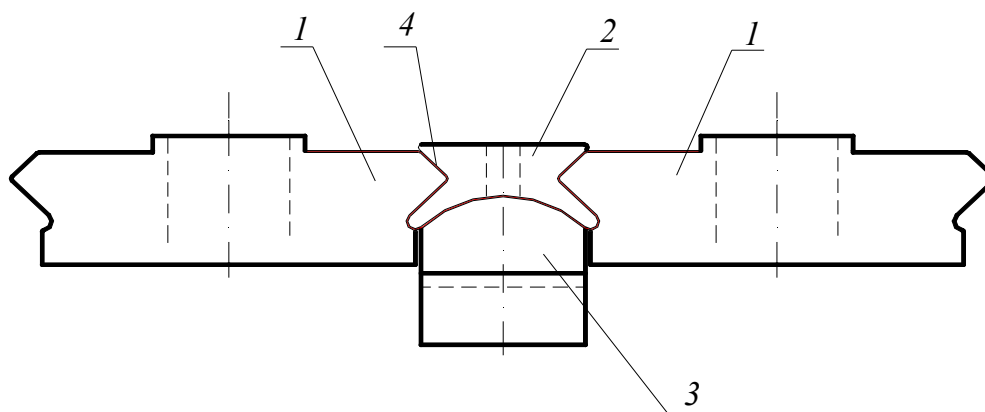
Пары промежуточные 1 – ролики промежуточные; 2 – фильера верхняя; 3 – фильера нижняя; 4 – профиль
